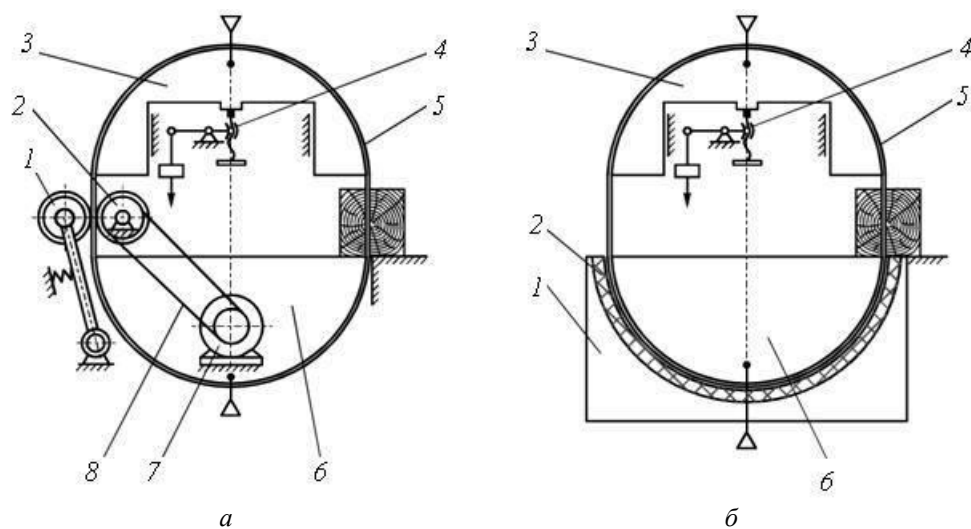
Схемы узла резания ленточнопильного станка с криволинейными аэростатическими направляющими: а – привод пилы с помощью фрикционных колес: 1 – прижимное фрикционное колесо; 2 – приводное фрикционное колесо; 3, 6 – верхняя и нижняя направляющие; 4 – механизм натяжения; 5 – пила; 7 – электродвигатель; 8 – ременная передача; б – привод с помощью линейного электродвигателя: 1 – корпус статора; 2 – обмотка двигателя; 3, 6 – верхняя и нижняя направляющие; 4 – механизм натяжения; 5 – пила
